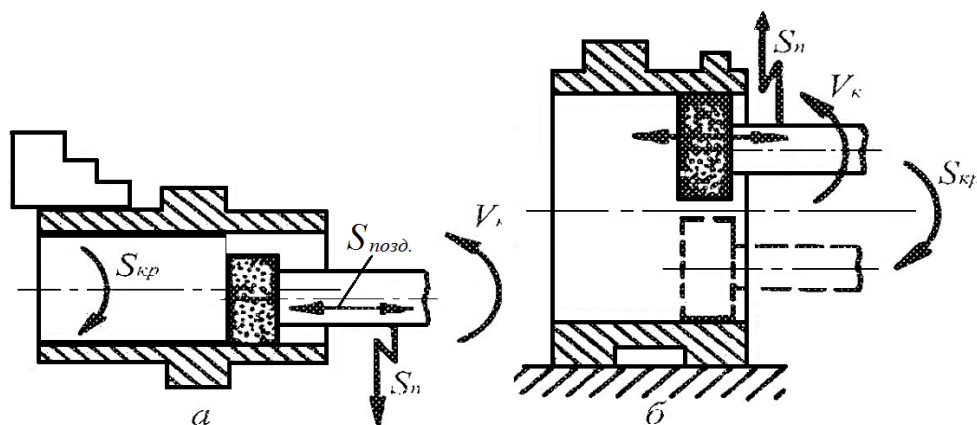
Схеми обробки заготовок на внутрішньошліфувальних верстатах
